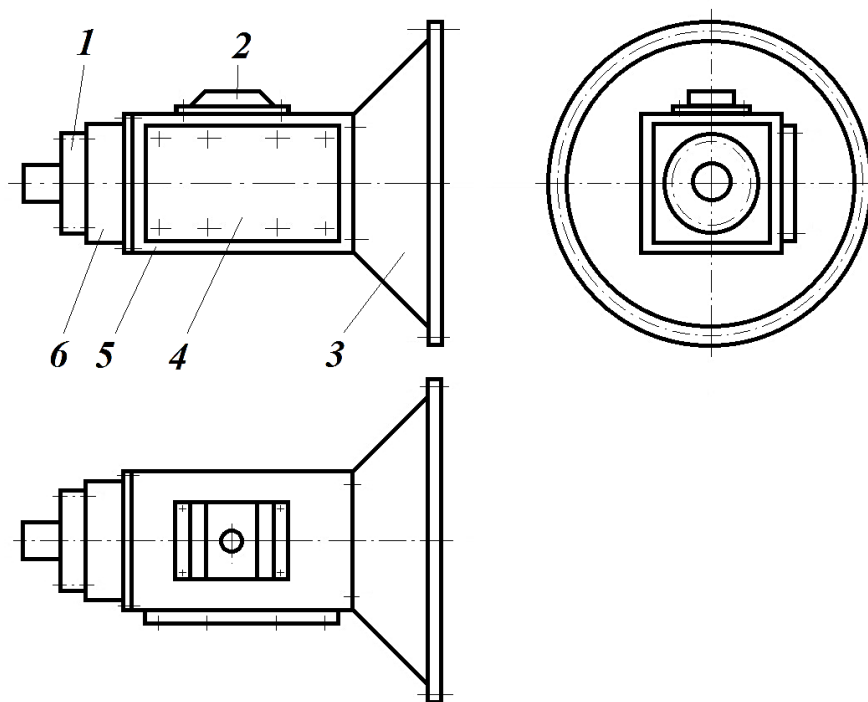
Стенд Р-641 для разборки и сборки агрегатов автомобилей
